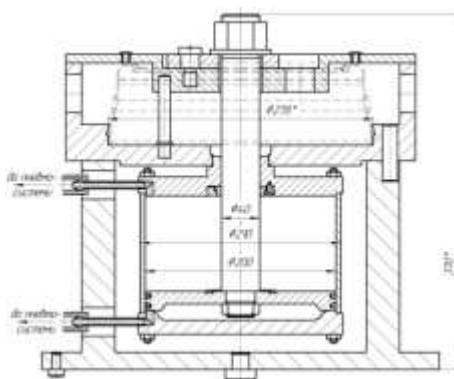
Ескіз робочого пристрою для свердлильної обробки
